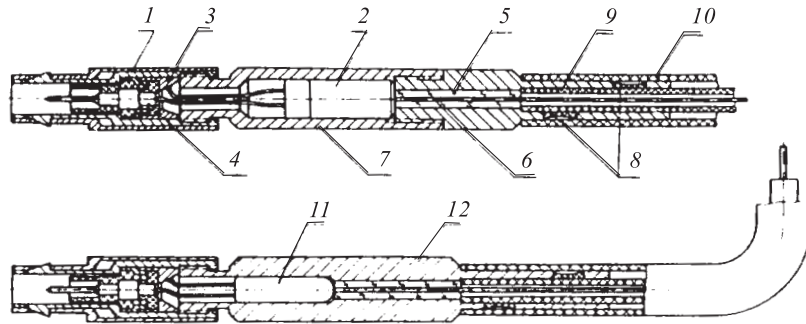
Активный разъемный соединитель с использованием электрического разъема «LEMO»: 1 — корпус; 2 — фотодиод; 3, 4 — точки электрических вводов; 5 — капилляр; 6–12 — наконечники; 7 — корпус приборной части; 8 — отверстия в хвостовике для нанесения клея; 9 — волоконно-оптический кабель; 10 — защитный кембрик; 11 — светодиод
